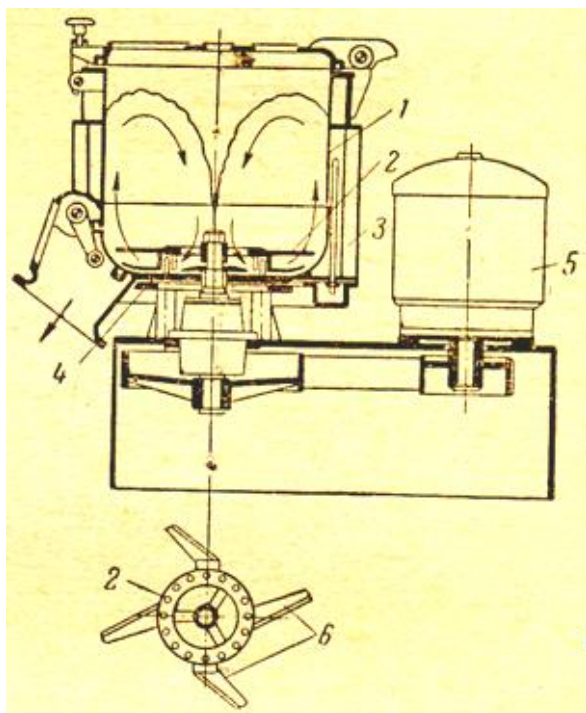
Циркуляційний змішувач: 1 – корпус; 2 – ротор; 3 – масляна сорочка; 4 – статор; 5 – електродвигун; 6 – лопаті ротора
